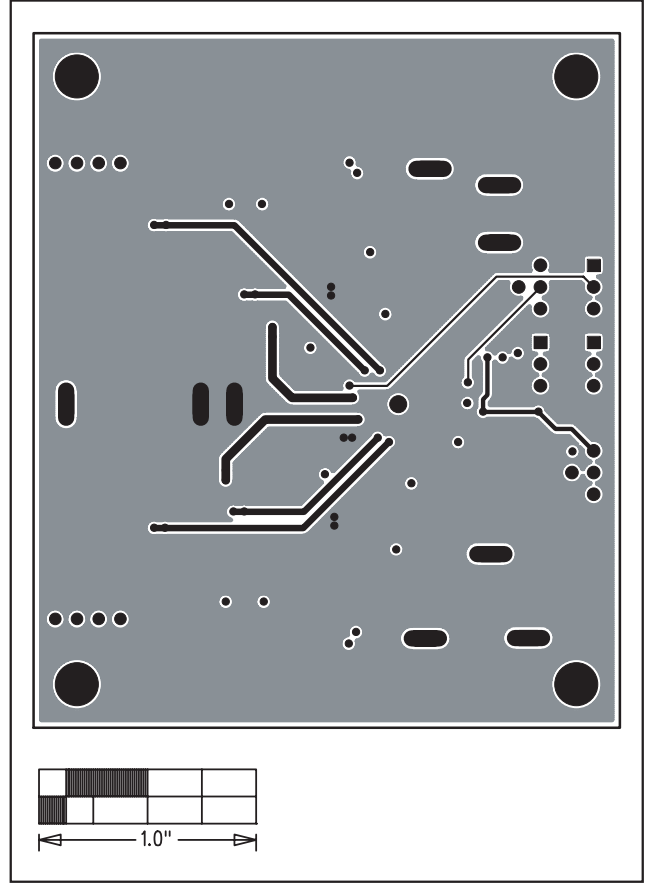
MAX1540 评估板 PCB 布局 – 接地层 2
